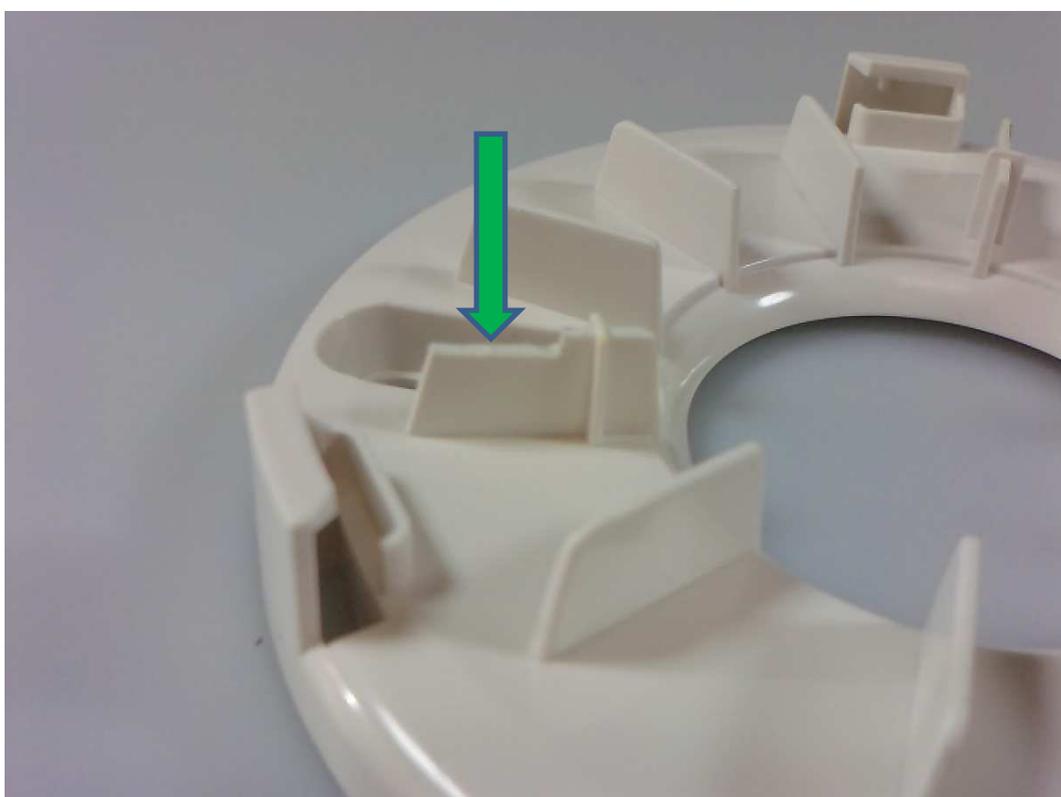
/ Montageplatte, Nahaufnahme des Stegs /
